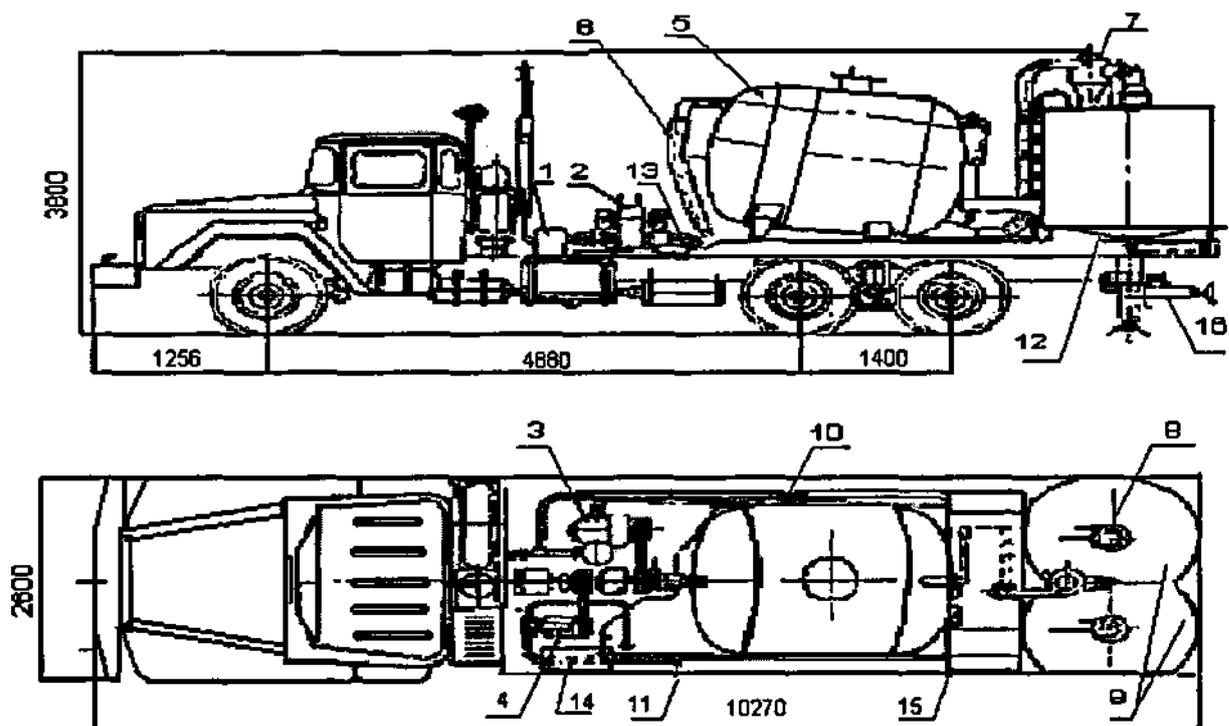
Установка для приготовления цементного раствора 6/6:
